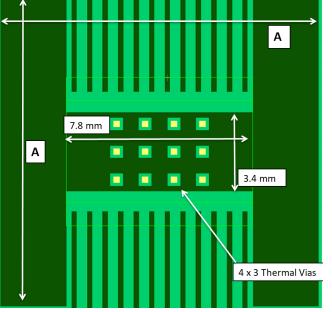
PCB - Top Layer (4/2-Layer PCB) for HTSSOP Package
